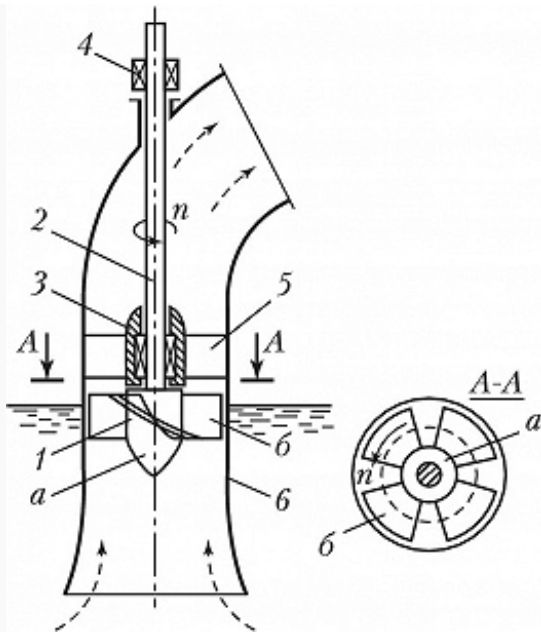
Схема осевого насоса: 1 – рабочее колесо (а – втулка, б – лопасть); 2 – приводной вал; 3 – нижний подшипник; 4 – верхний подшипник; 5 – выправляющий а...
